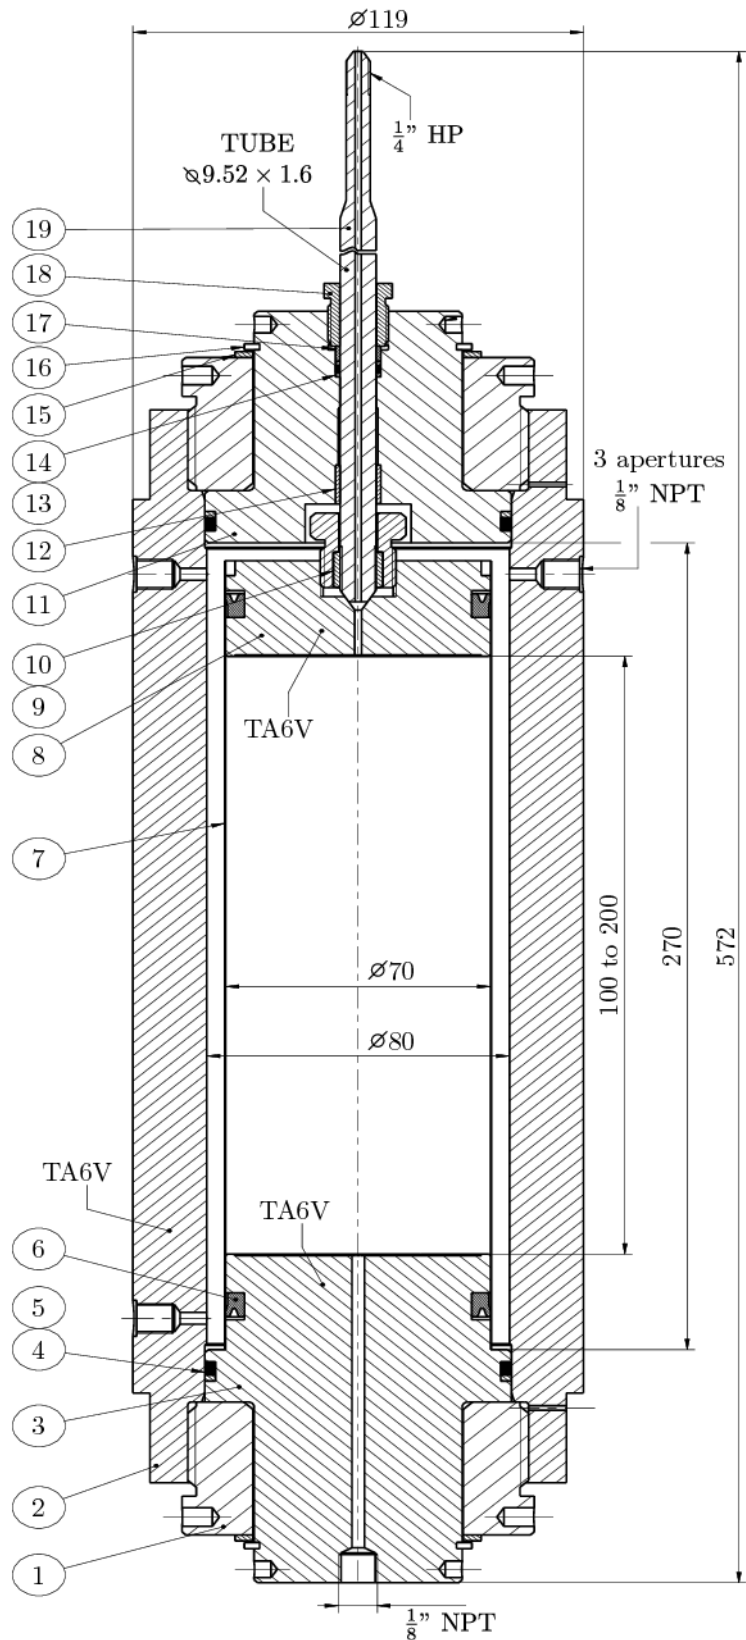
Dessin technique de la cellule Hassler spécifique aux neutrons [Yehya et al. 2018]
